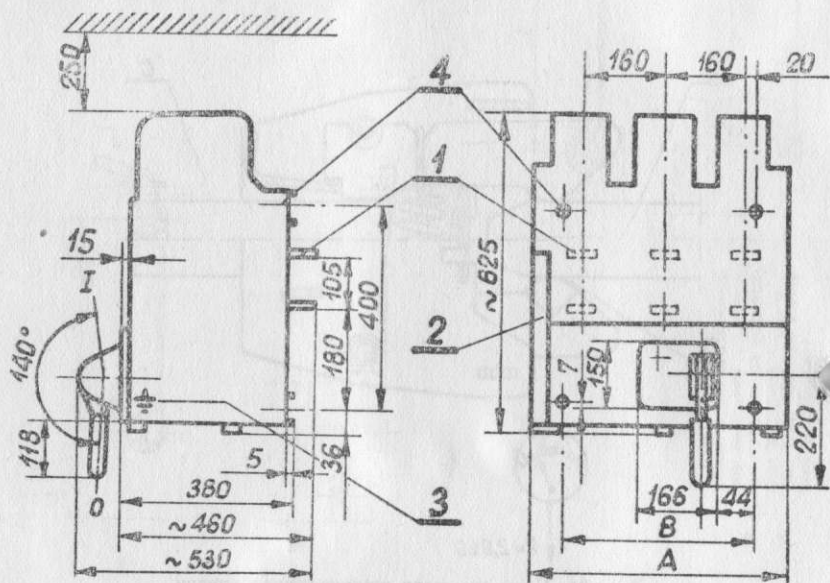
Размеры выключателей типа АРУ-50А с ручным передним приводом
